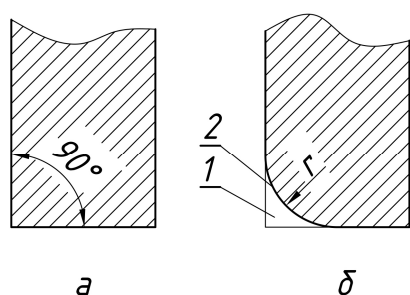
Профиль рабочей поверхности плоского ножа:
